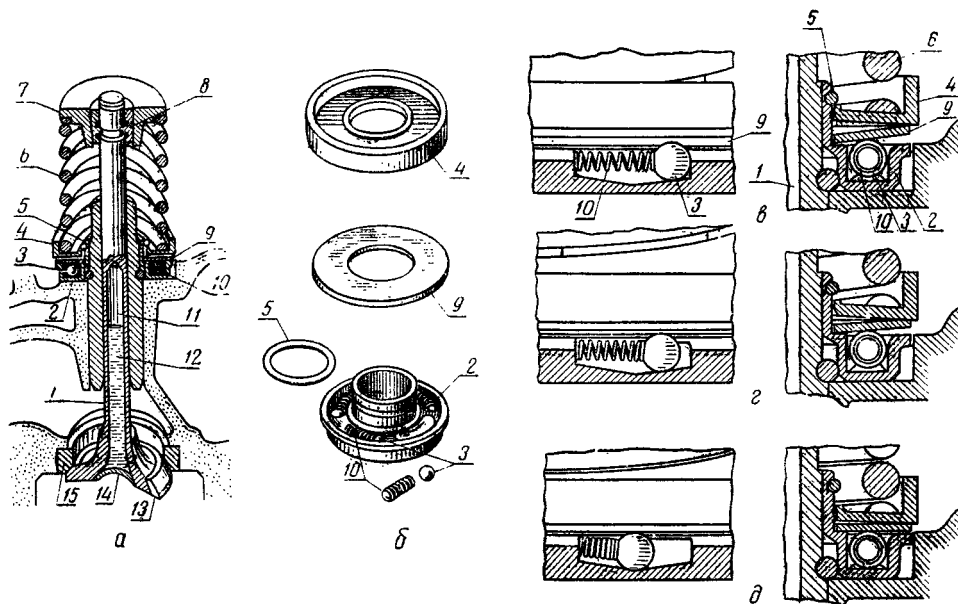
Выпускной клапан в сборе механизма газораспределения двигателя ЗИЛ-130 и схема поворота клапана:
